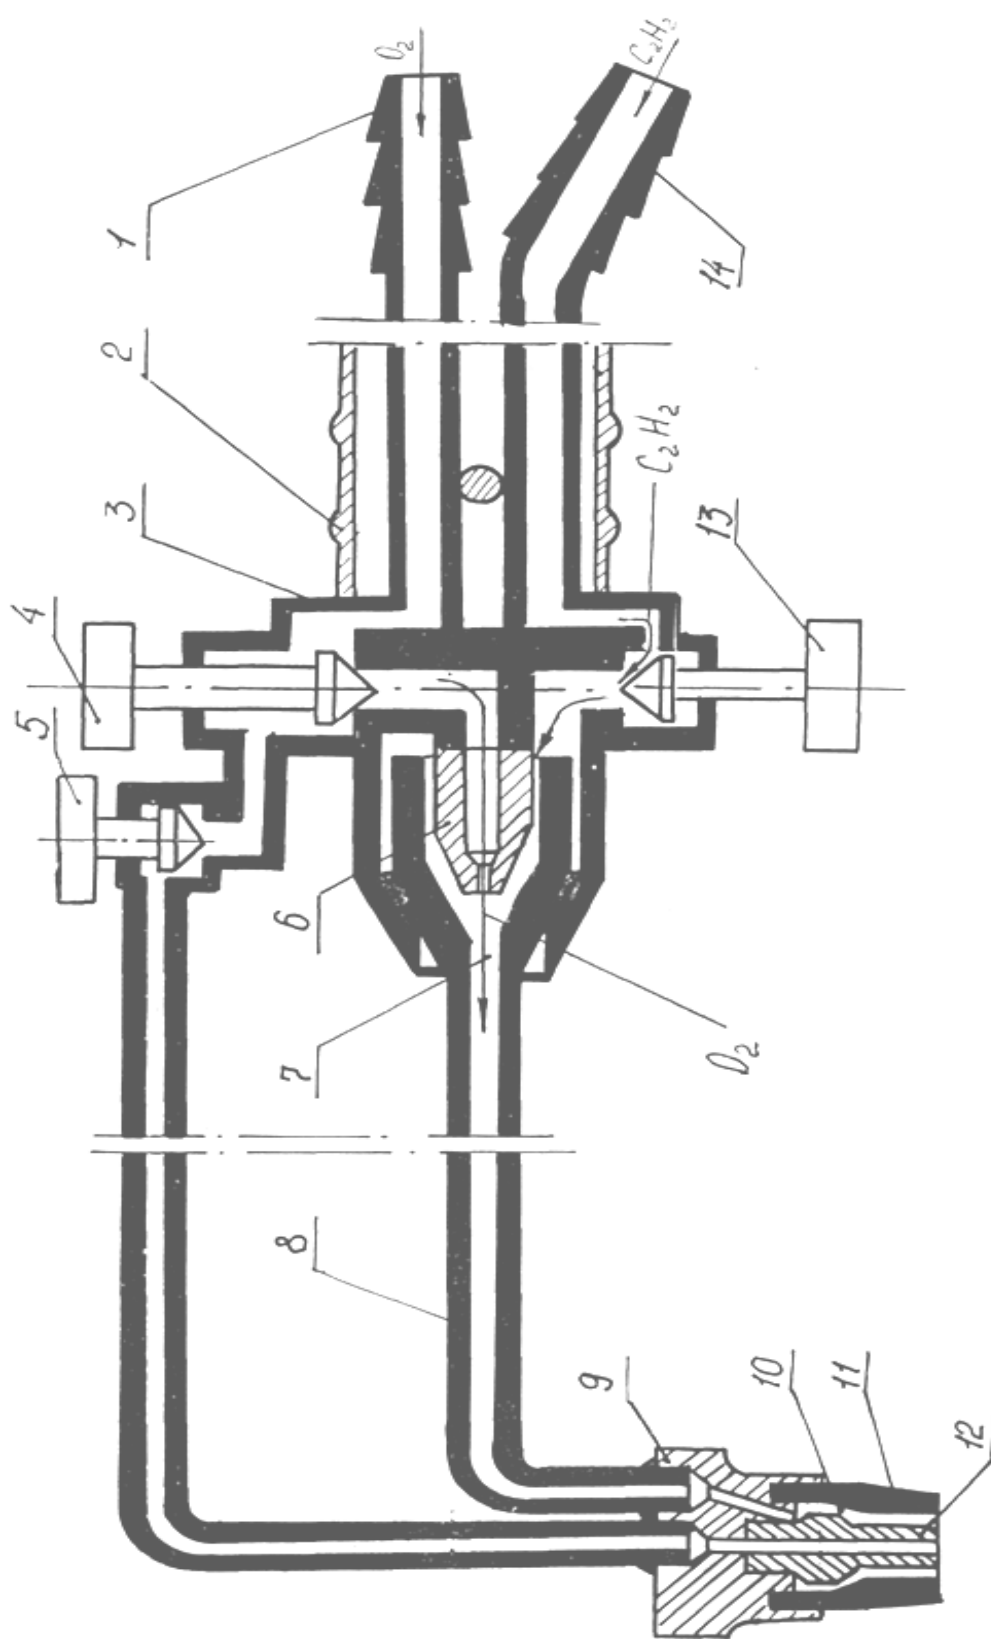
Схема инжекторного резака: 1 - ниппель; 2 - рукоятка резака; 3 - ствол резака; 4 - вентиль; 5 - вентиль режущего кислорода; 6 - инжектор; 7 - смесительная камера; 8 - трубка; 9 - головка; 10 - зазор для прохождения подогревающего пламени; 11 - наружный мундштук; 12 - внутренний мундштук; 13 - вентиль; 14 - ниппель
